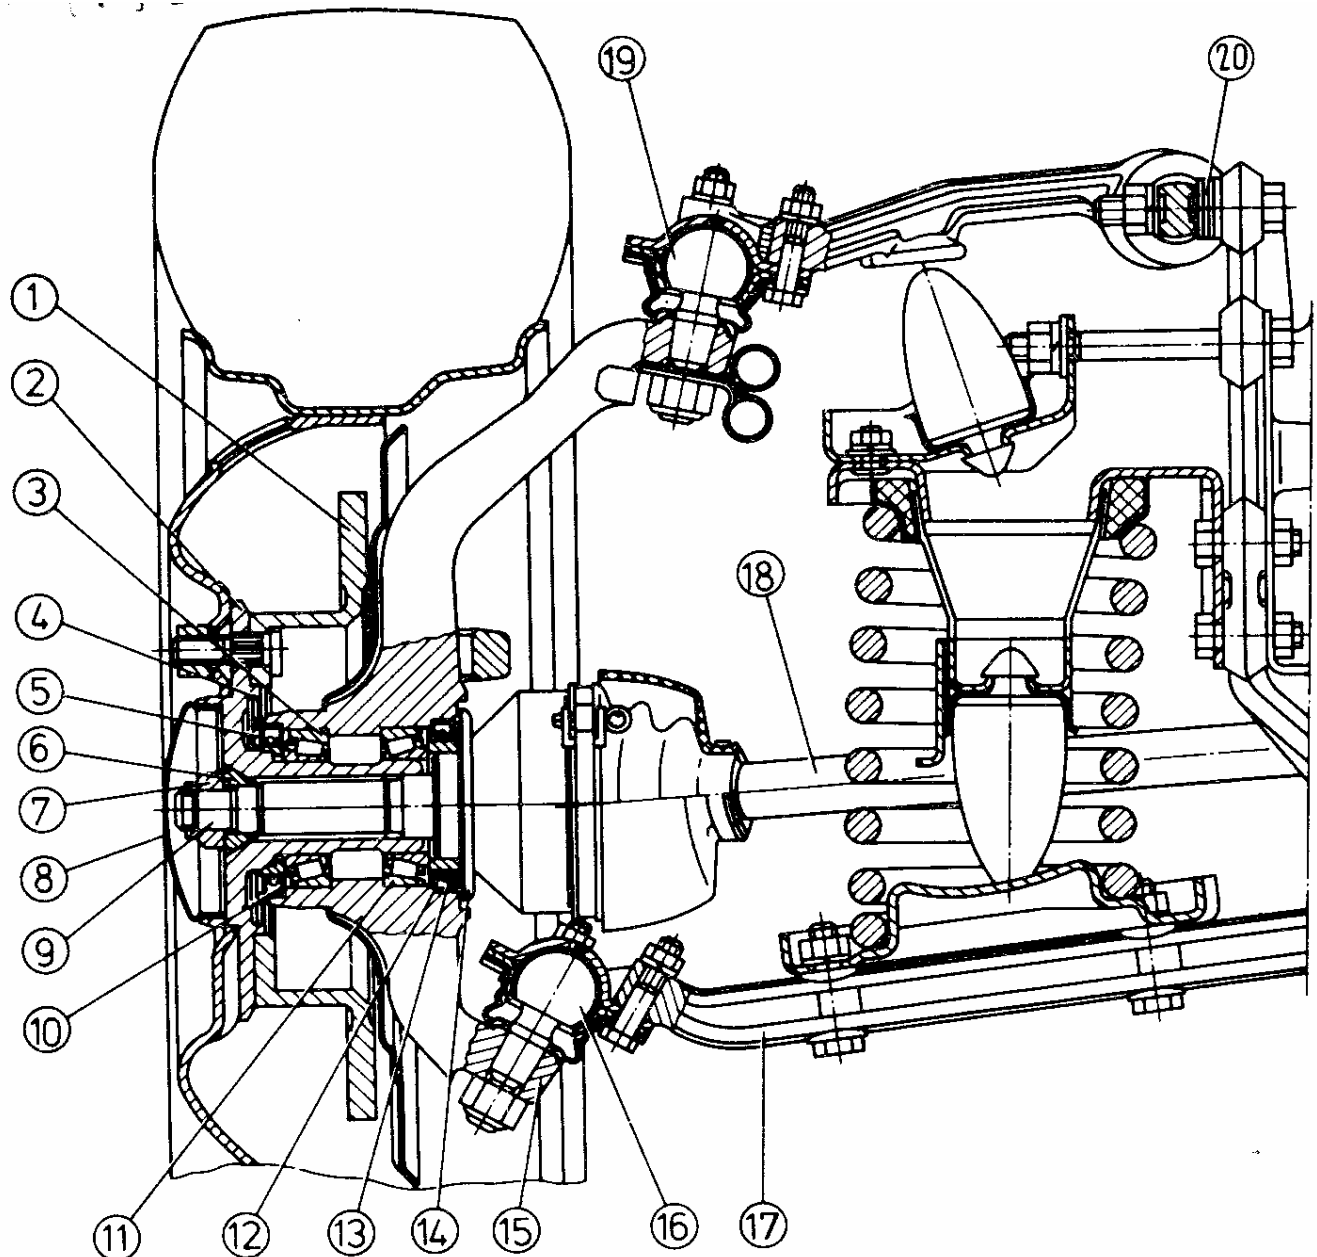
Rueda delantera: 1 - disco de freno; 2- cubo; 3- cojinete exterior de rodillos; 4- anillo de protección del retén exterior; 5- retén exterior; 6- casquillo cónico; 7- tuerca de sujeción del cubo; 8- capacete del cubo; 9- espiga del árbol cardánico; 10- anillo de desmontaje del retén exterior; 11 - cojinete interior de rodillos; 12- anillo de desmontaje del retén interior; 13- retén interior; 14- anillo de protección del retén interior; 15- mangueta; 16- rótula de la palanca inferior; 17- palanca inferior; 18- árbol cardánico; 19- rótula de la palanca superior; 20- juego de juntas
